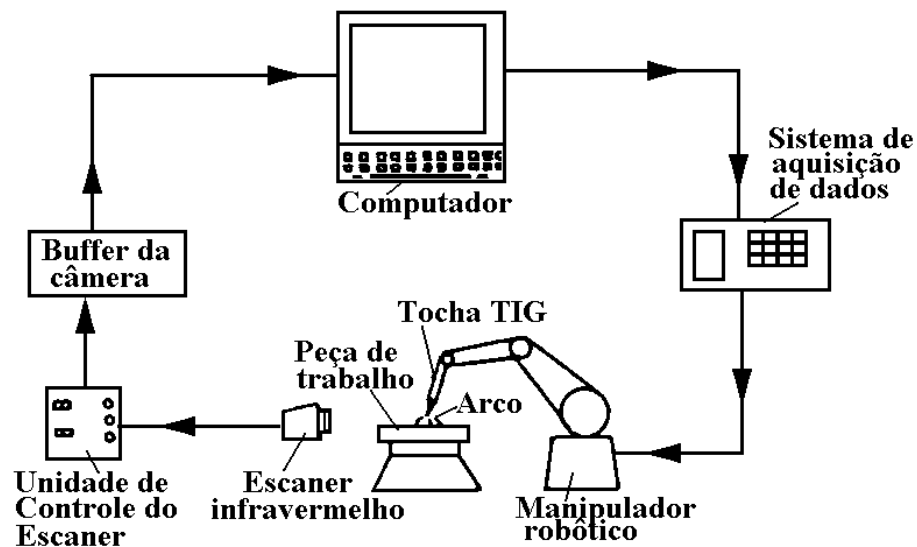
Componentes essenciais de um sistema de Robô com solda MIG
